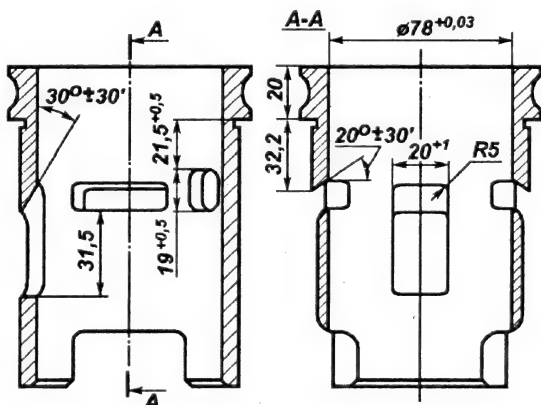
Гильза цилиндра двигателя мотора «Вихрь-30»
